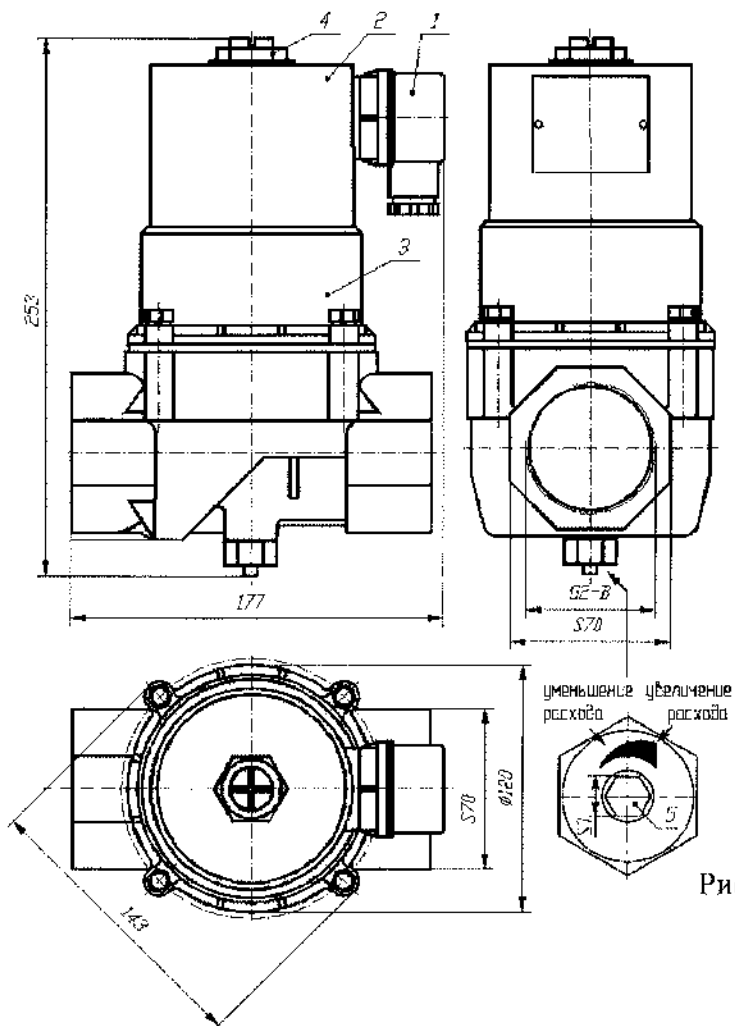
Габаритные и установочные размеры клапана КИ 90-10
